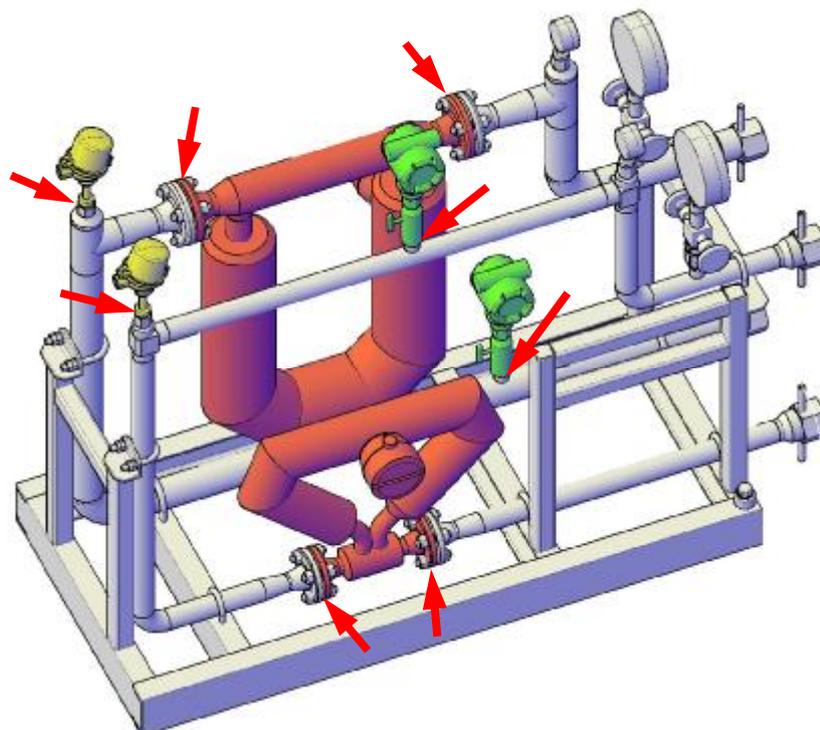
Места пломбировки установки поверочной передвижной УПП
